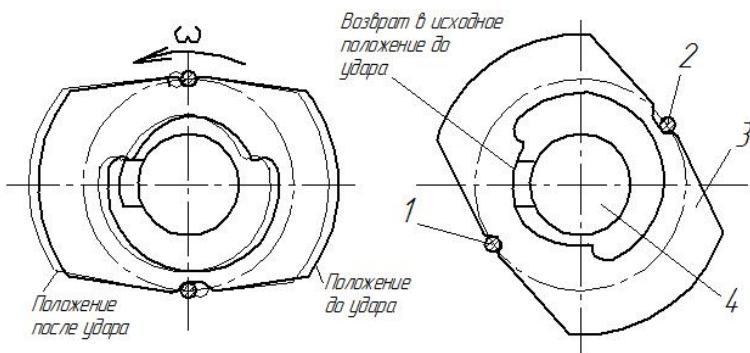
Схема работы ударного гайковерта (условно вал остается неподвижным): 1 – ведущий палец; 2 – поддерживающий палец; 3 – шайба-молоток; 4 – вал головки торцевого ключа с упором
